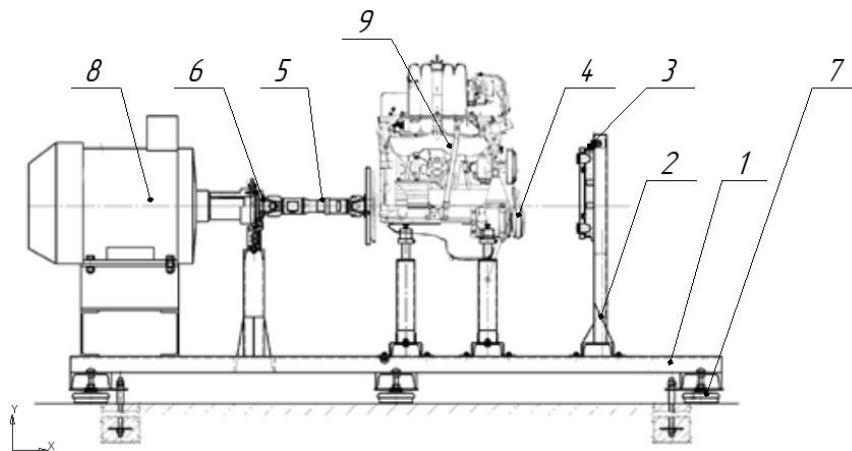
Стенд для обкатки ДВЗ: 1 – рама станду; 2 – кронштейн радіатора; 3 – радіатор; 4 – гвинтова опора; 5 – карданний вал станду; 6 – датчик крутного моменту; 7 – віброізолюючі опори, 8 – приводний електродвигун, 9 – випробуваний ДВЗ.
